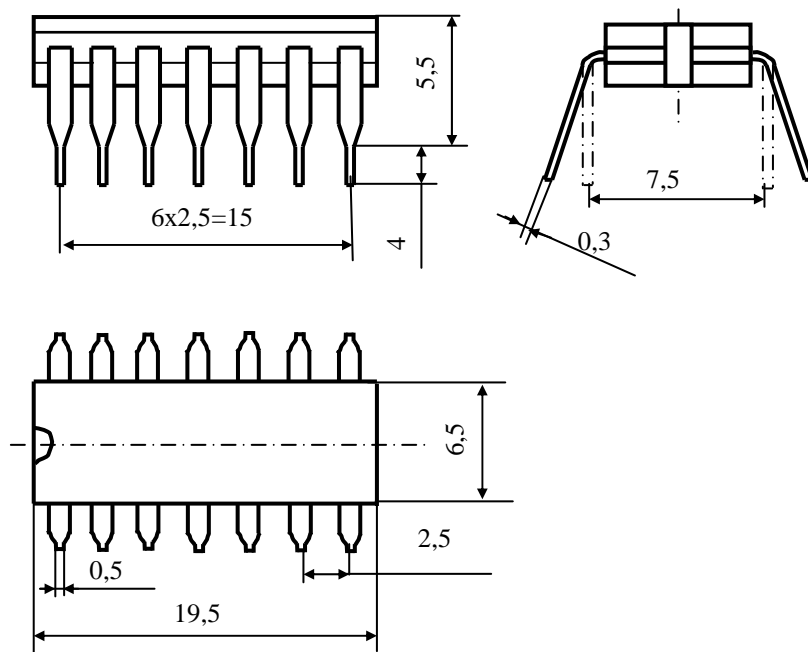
Внешний вид и габаритные размеры цифровой микросхемы в корпусе 201.14-1, 201.14-6
